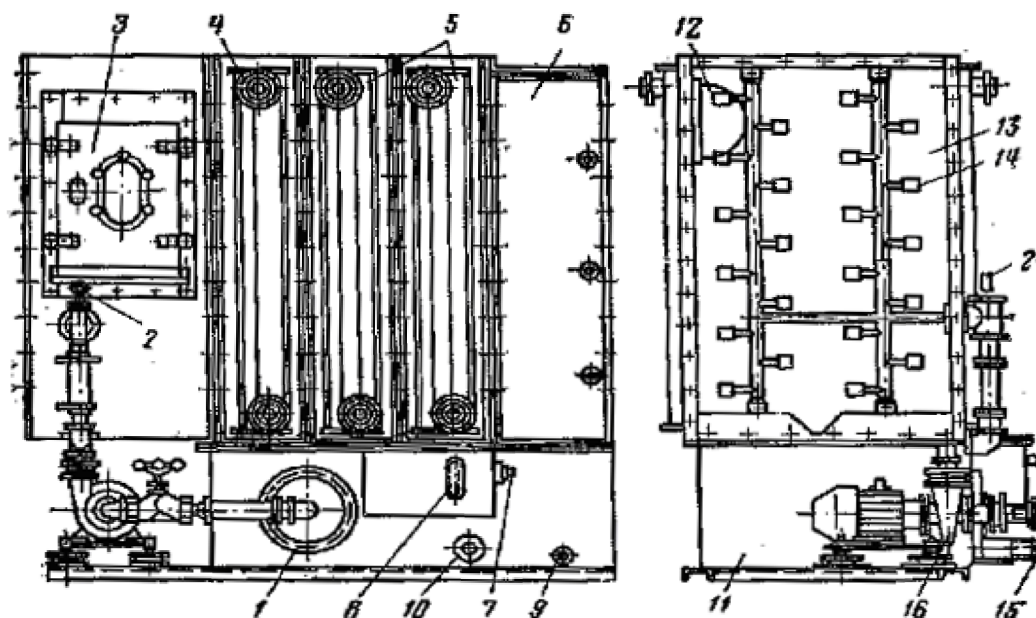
Типовой поверхностный орошаемый воздухоохладитель.
